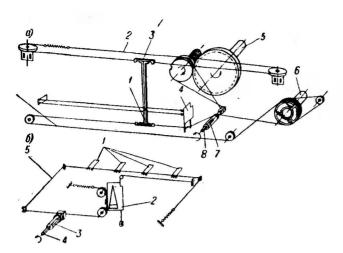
Кинематическая схема верньерного устройства магнитол «Миния-3» и «Миния-4»
